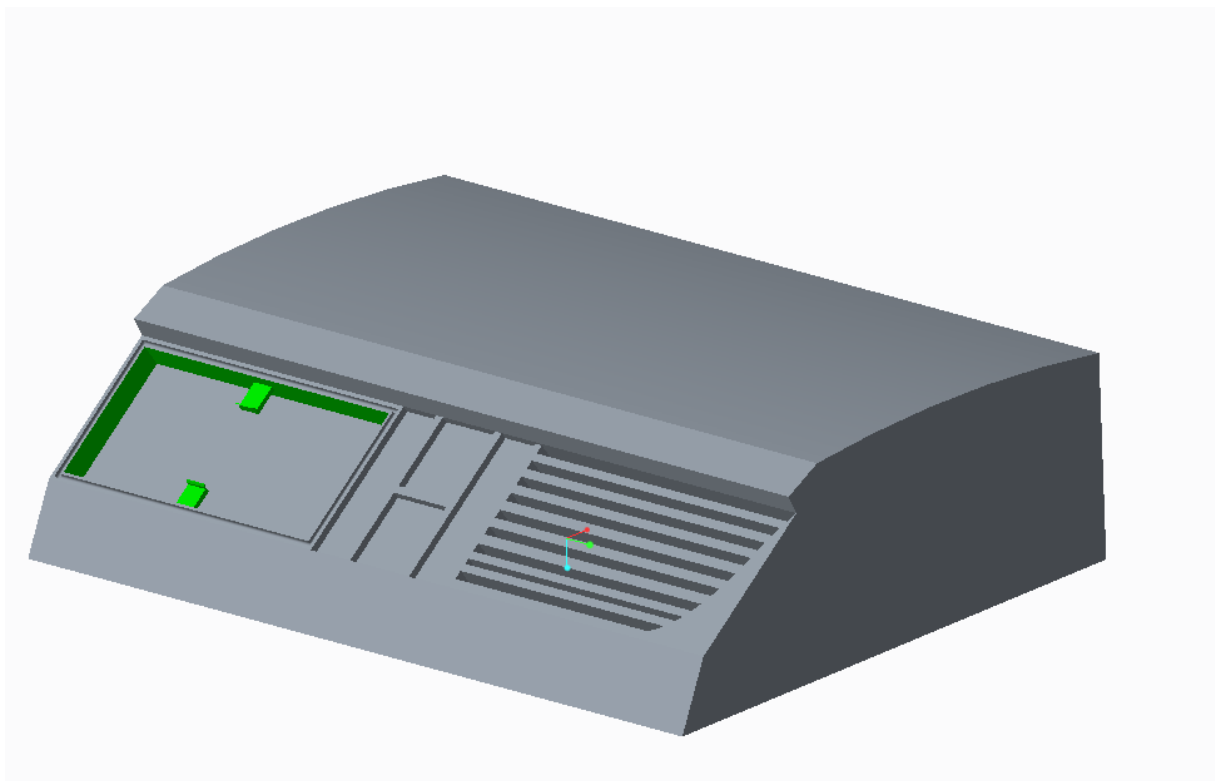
Držák zasunutý přímo do záhybu palubové desky
